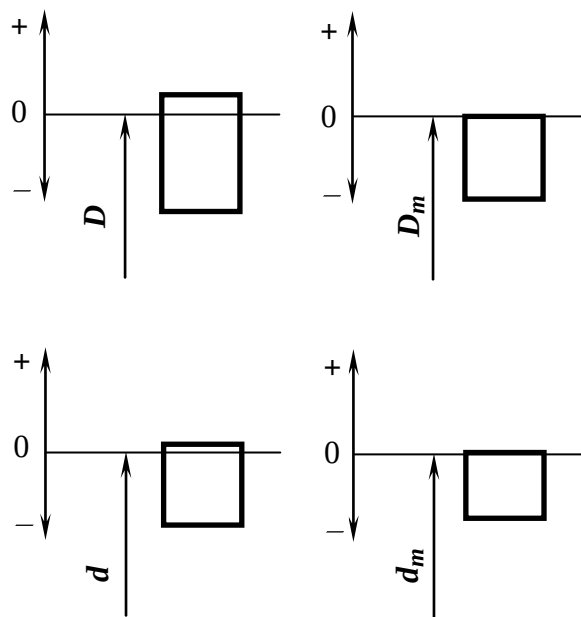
Схемы полей допусков диаметров D и D_m наружного кольца и d и d_m внутреннего кольца подшипника качения
